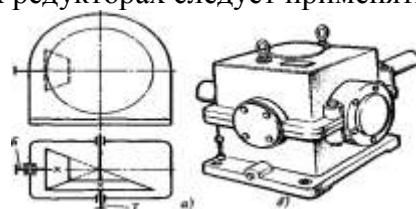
Одноступенчатый редуктор с коническими зубчатыми колесами:
